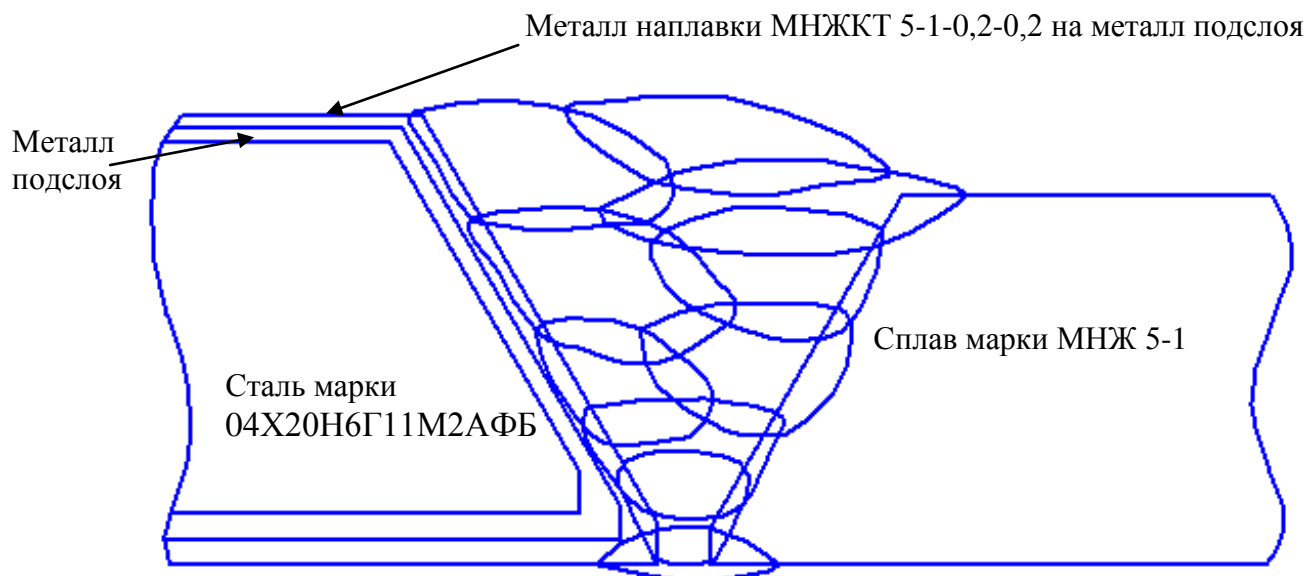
Схема сварки V-образного сварного соединения сплава марки МНЖ 5-1 со сталью 04Х20Н6Г11М2АФБ через подслоя, наплавленный проволокой ЭП-263Ш
